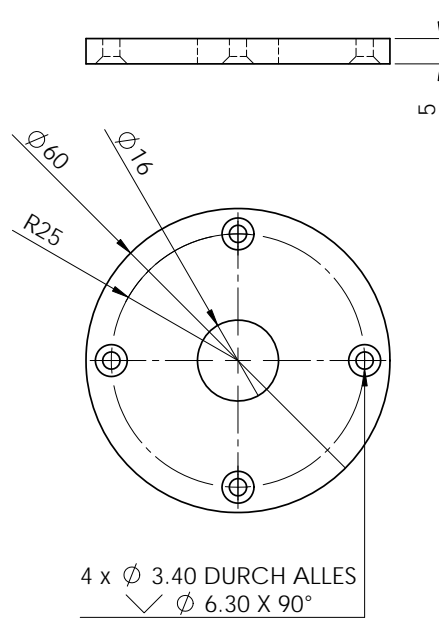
Technische Zeichnung des Detektorflansch-Gegenstücks.
